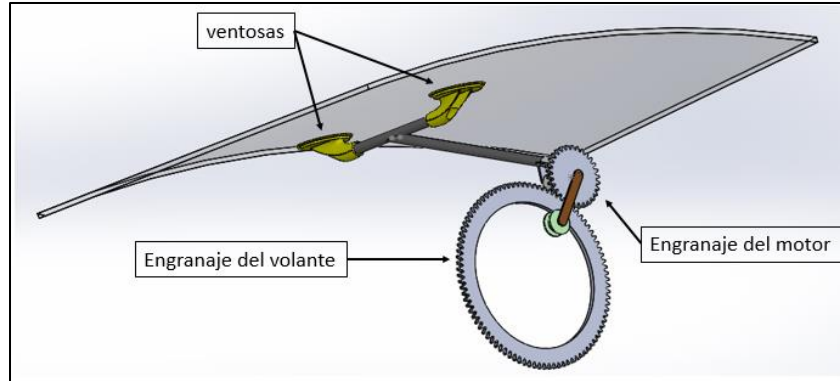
modelo 3.1 diseño de los engranajes (fuente: diseño propio).
